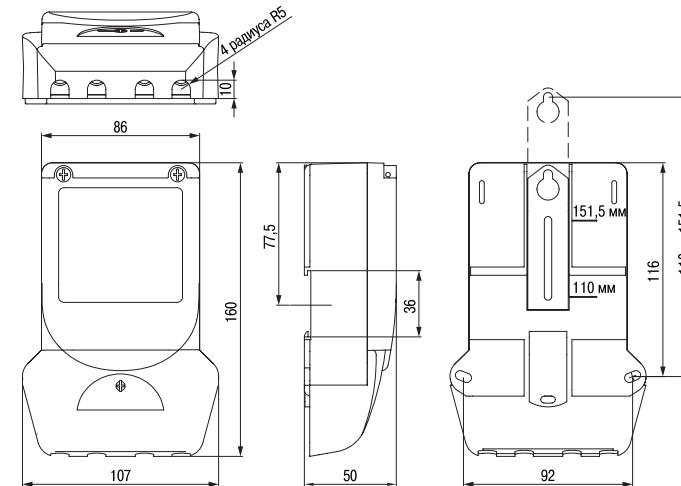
Габаритные и присоединительные размеры счётчиков габарита корпуса 3
